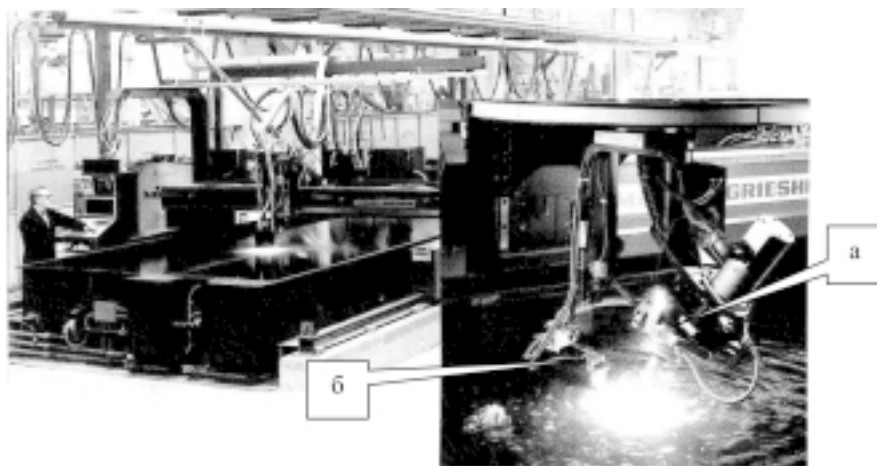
Машина термической резки металла фирмы «Мессергрисхейм» для вырезки деталей с одновременной разделкой кромок под сварку: а – поворотный плазменный резак; б – устройство для нанесения разметки
